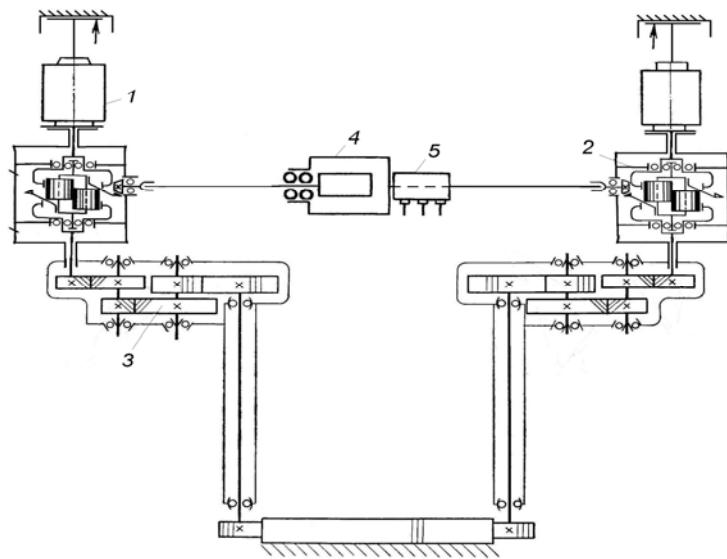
Кинематическая схема двухдвигательного привода механизма поворота драглайна инновационной конструкции: 1 - электродвигатель постоянного тока; 2 - трёхзвенный дифференциал 2К-Н; 3 - редуктор базовой конструкции привода; 4 - гидромашина; 5 - гидроколлектор
